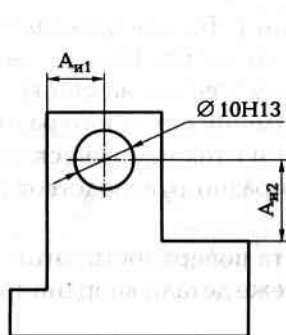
Эскиз обрабатываемой детали к заданию 1.28
